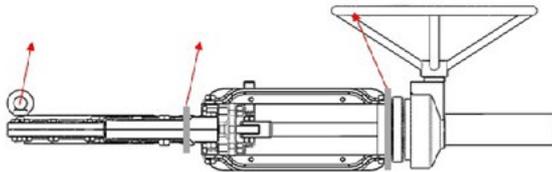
Válvula de Cuchilla con Actuador de Engranes Cónicos, Elevación Horizontal
